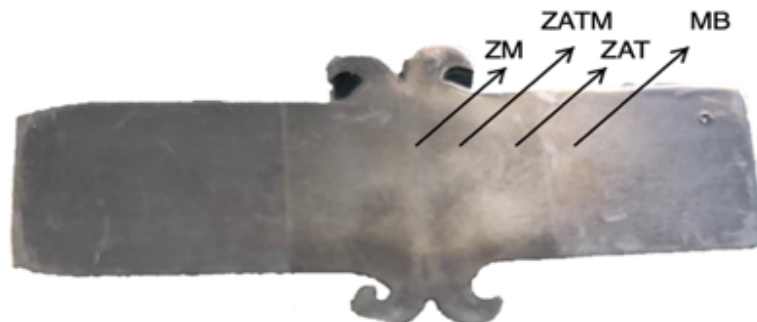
Zonas afectadas por el calor en una probeta soldada por soldadura por fricción rotacional.
